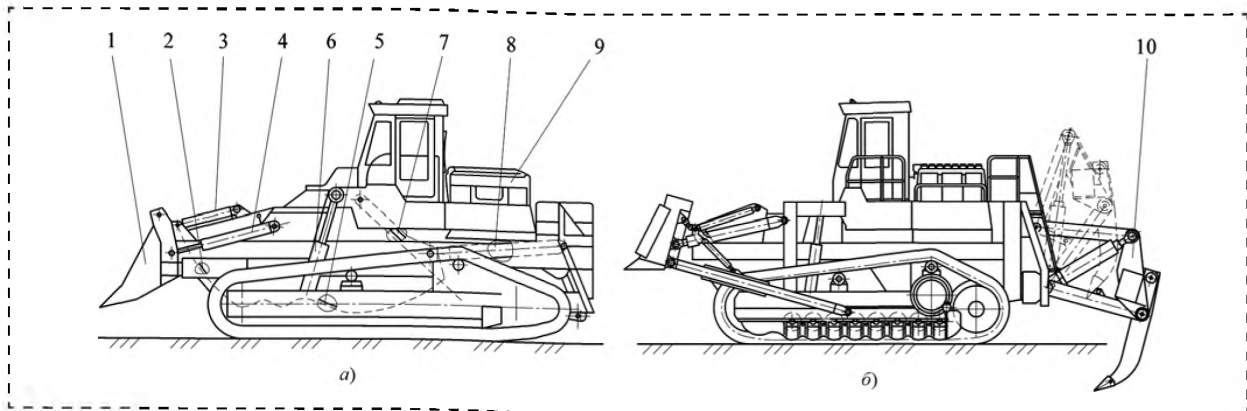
Конструктивные схемы бульдозерно-скреперного агрегата (а) и возможного в перспективе бульдозерно-скреперно-рыхлительного агрегата (б): 1 – отвал; 2 – заслонка; 3 – гидроцилиндр поворота заслонки; 4 – гидроцилиндр поворота отвала; 5 – ковш; 6 – гидроцилиндр подъема опускания ковша; 7 – поворотная задняя стенка; 8 – гидроцилиндр поворота стенки; 9 – силовая установка; 10 – рыхлительное оборудование
